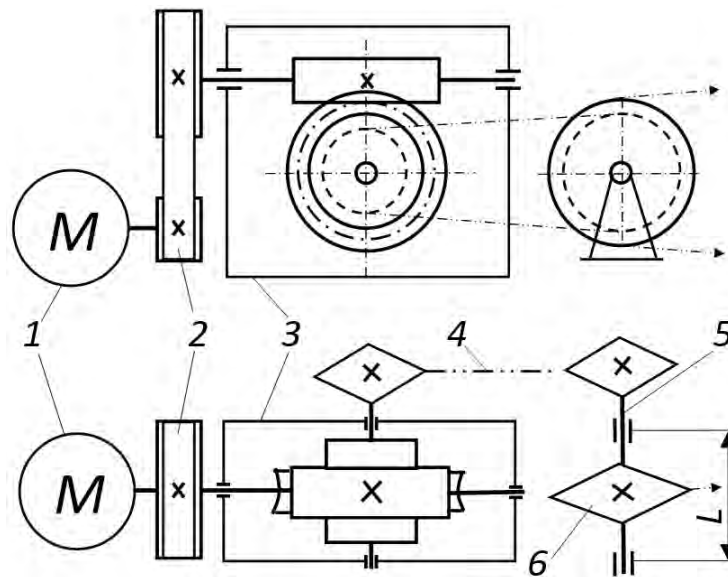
Схема привода скребкового конвейера (фронтальный вид и вид сверху):
